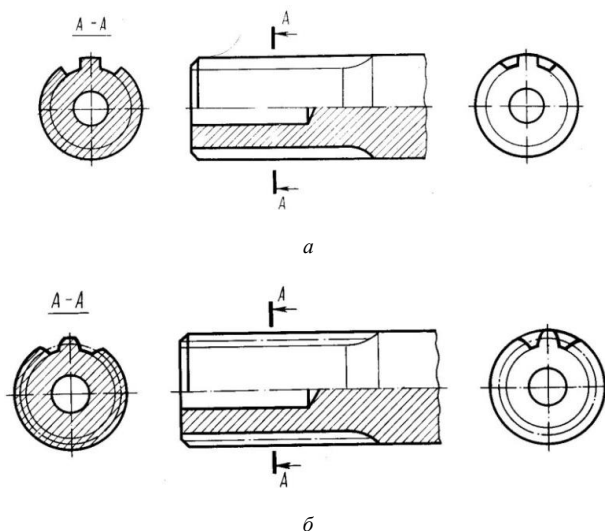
Шлицевой вал: *a* – прямобочный; *б* – эвольвентный
